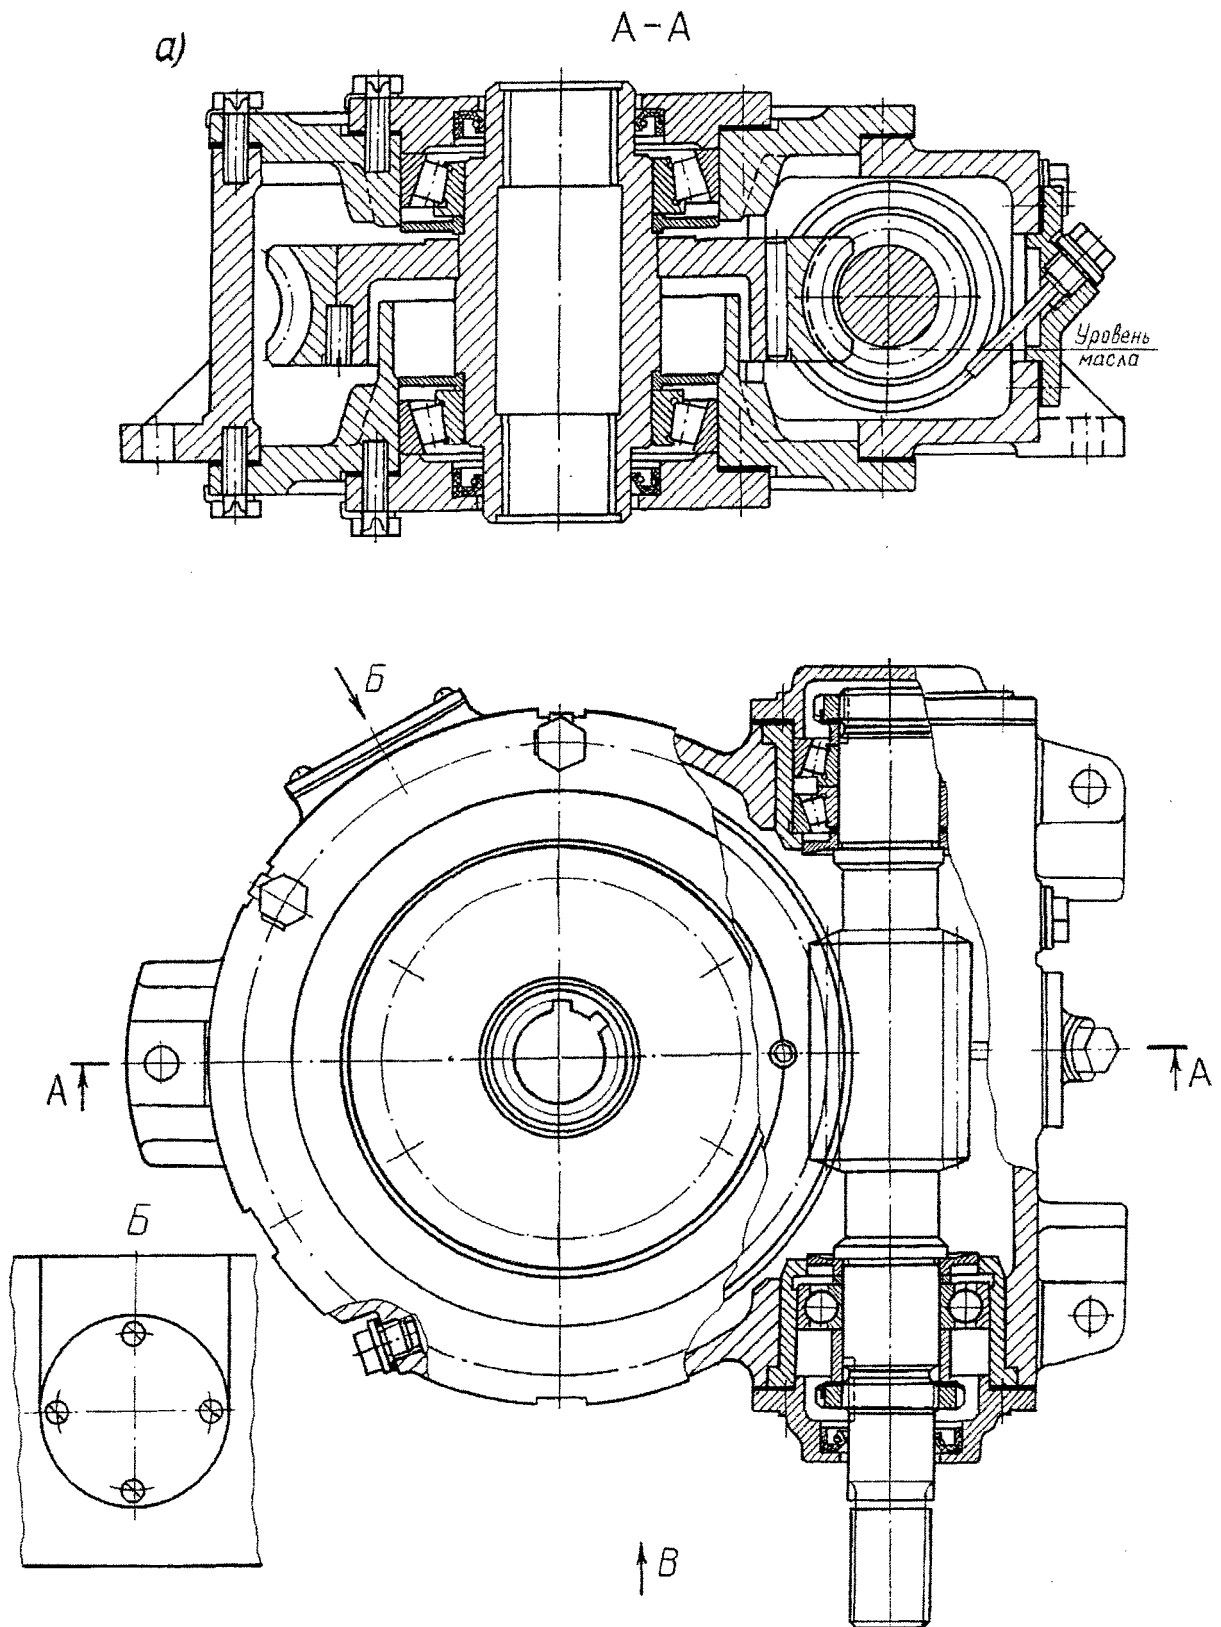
Одноступенчатый червячный редуктор специального назначения с полым тихоходным валом
